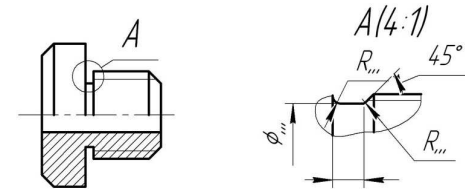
в. Зображення фасок та нарізевої проточки при виконанні робочого кресленика деталі
